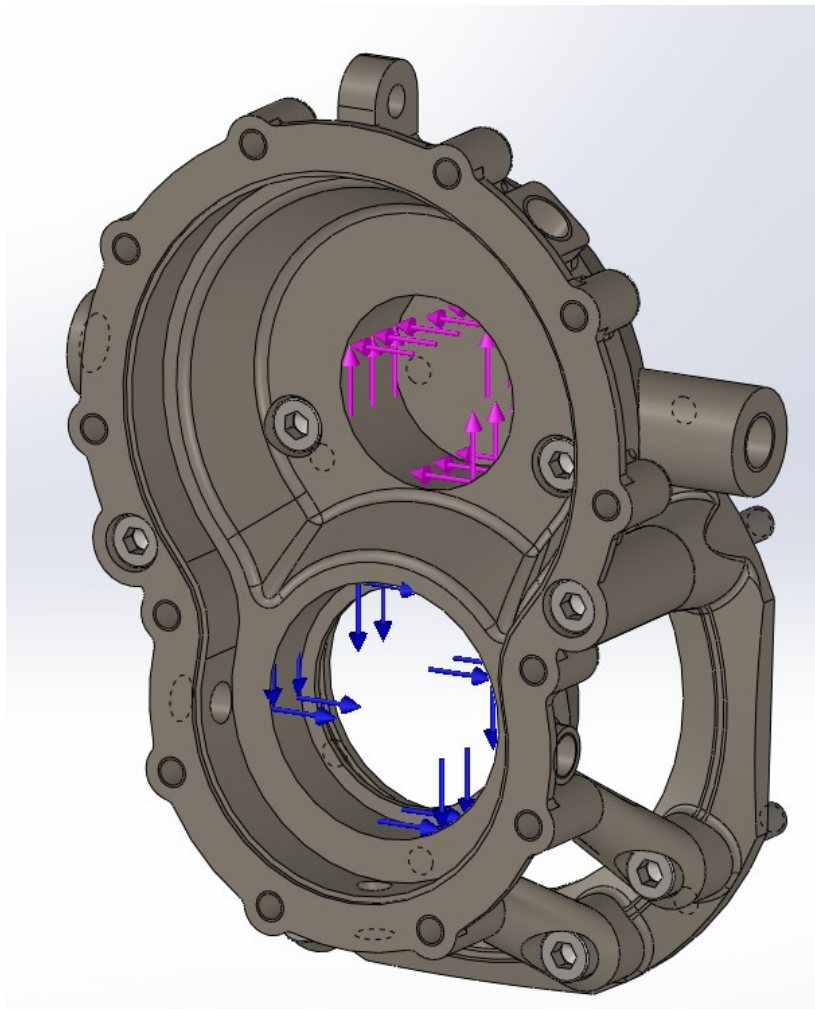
Carter lato motore con carichi da cuscinetto –
